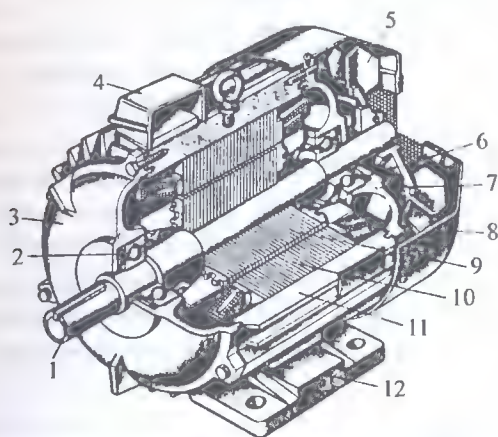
Трехфазный асинхронный двигатель серии 4А с короткозамкнутым ротором: 1 — вал; 2, 6 — подшипники; 3, 7 — подшипниковые щиты; 4 — коробка выводов; 5 — вентилятор; 8 — кожух вентилятора; 9 — магнитопровод ротора с короткозамкнутой обмоткой; 10 — магнитопровод статора с обмоткой; 11 — корпус; 12 — лапы
